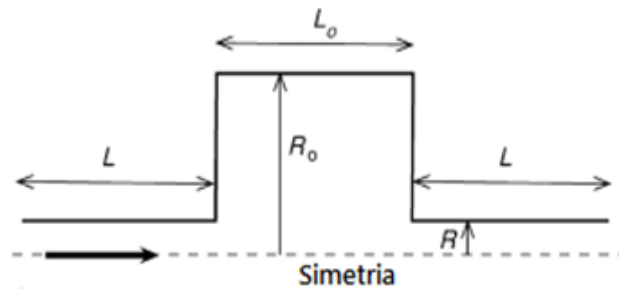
Canal de moldagem e solidificação para um polímero.
